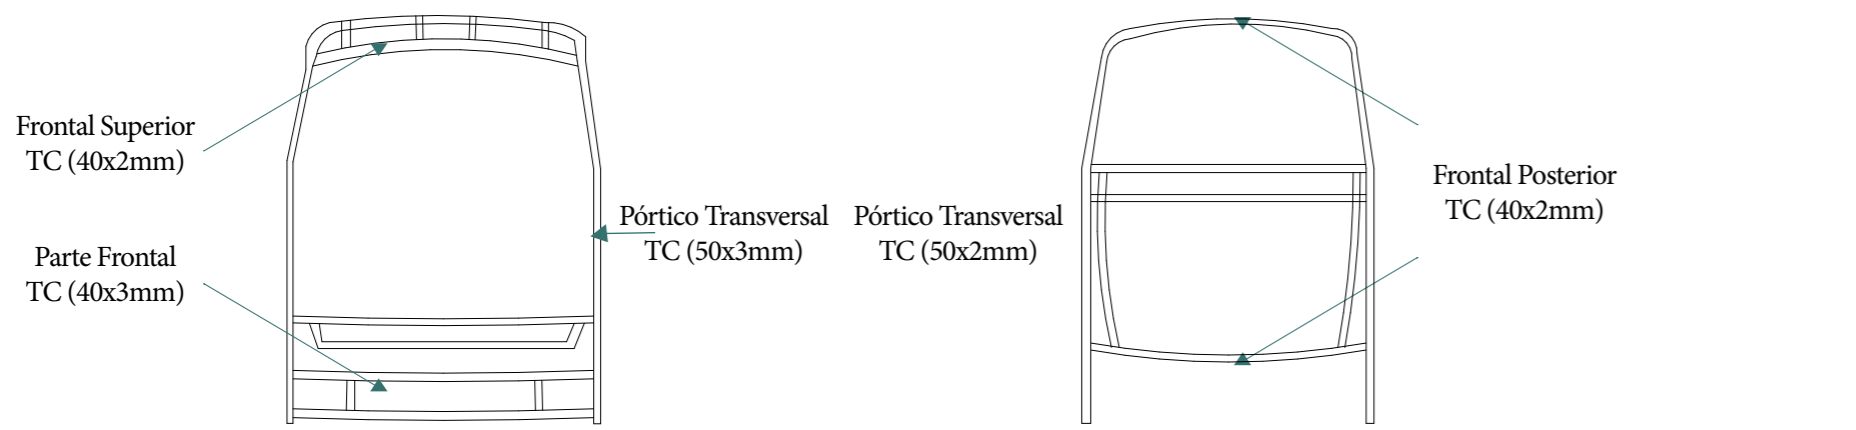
Imágen_ Ubicación de Tipos de perfiles estructurales en la carrocería de bus Fuente : (Villafuerte, 2017)
